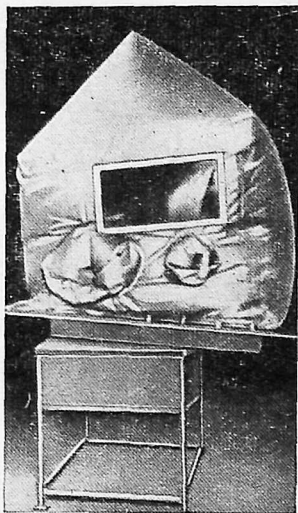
Общий вид мягкой газонаполненной сварочной камеры.
